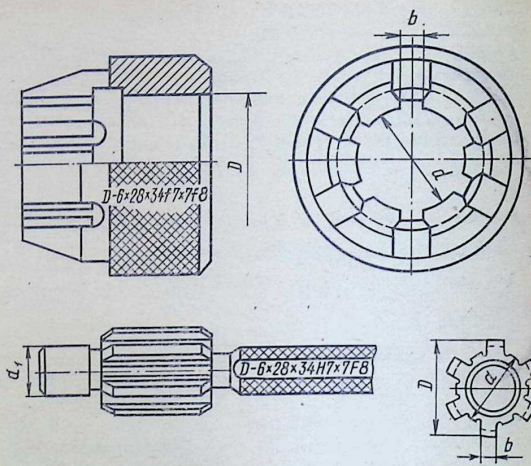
Комплексные калибры для контроля деталей шлицевых соединений.
